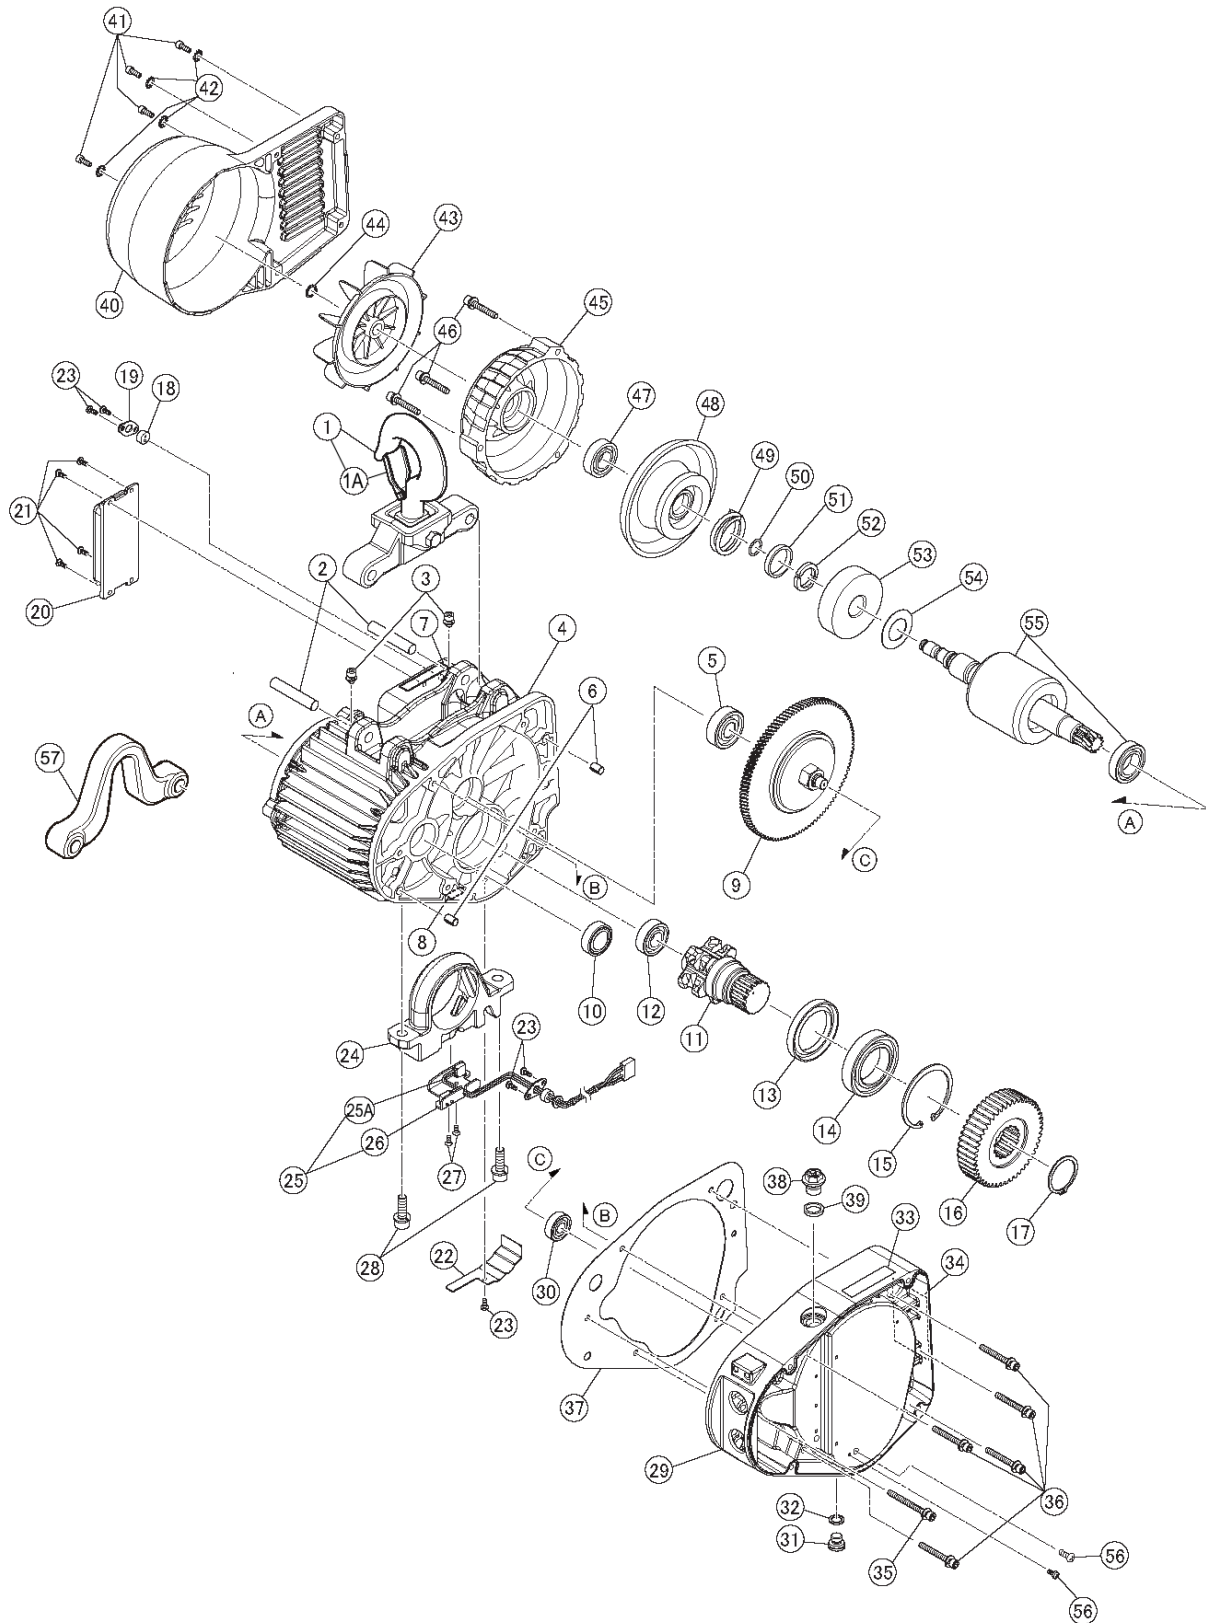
Pièces du boîtier, de l'engrenage et du moteur
